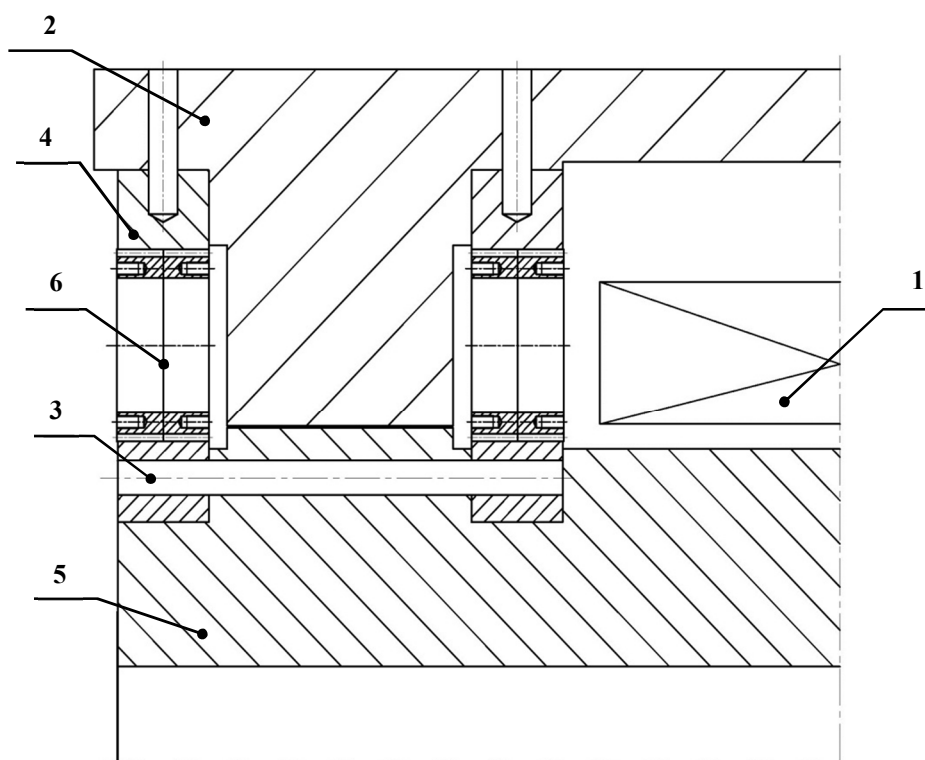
Схема УЭМ с катящимся зубчатым токосъёмом: 1 – обмотка возбуждения; 2 – магнитопровод статора; 3 – обмотка якоря; 4 – шестерня; 5 – магнитопровод ротора; 6 – разрезные сателлиты
